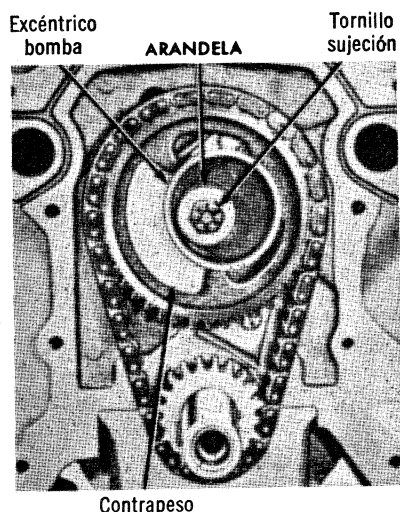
Excéntrico de Bomba Instalado. Típico
